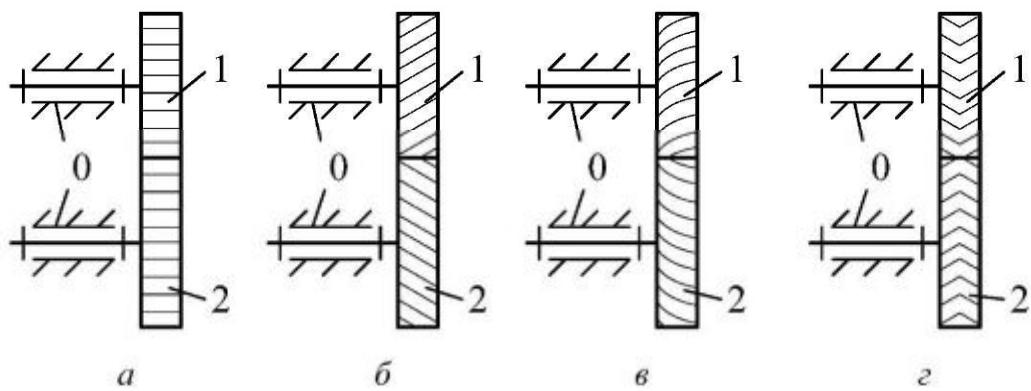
Схемы форм линии зуба простых зубчатых механизмов
